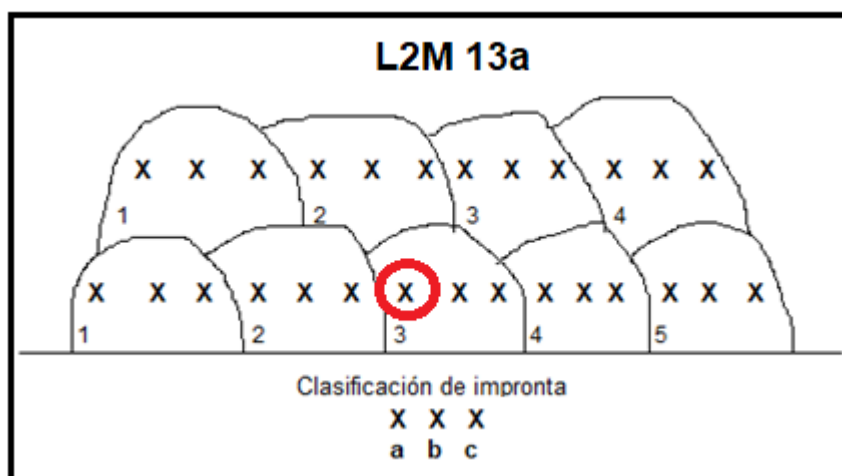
Geometría referencial de los cordones de soldadura.
